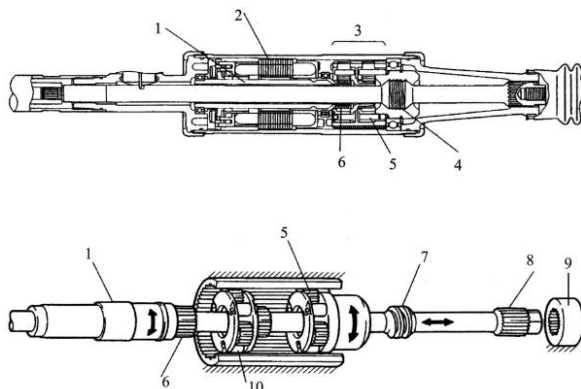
Электромеханический исполнительный механизм поворота задней оси:
